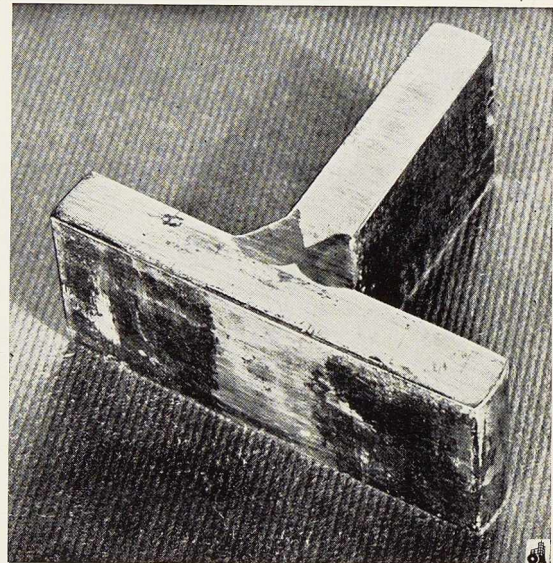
Eprouvettes de traction et de pliage sur joint soudé.
